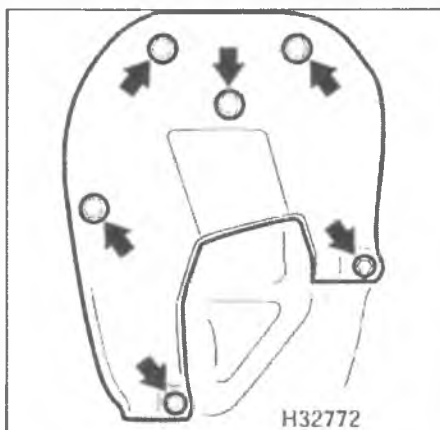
Выверните болты крепления верхней крышки газораспределительного механизма (отмечены стрелками)
